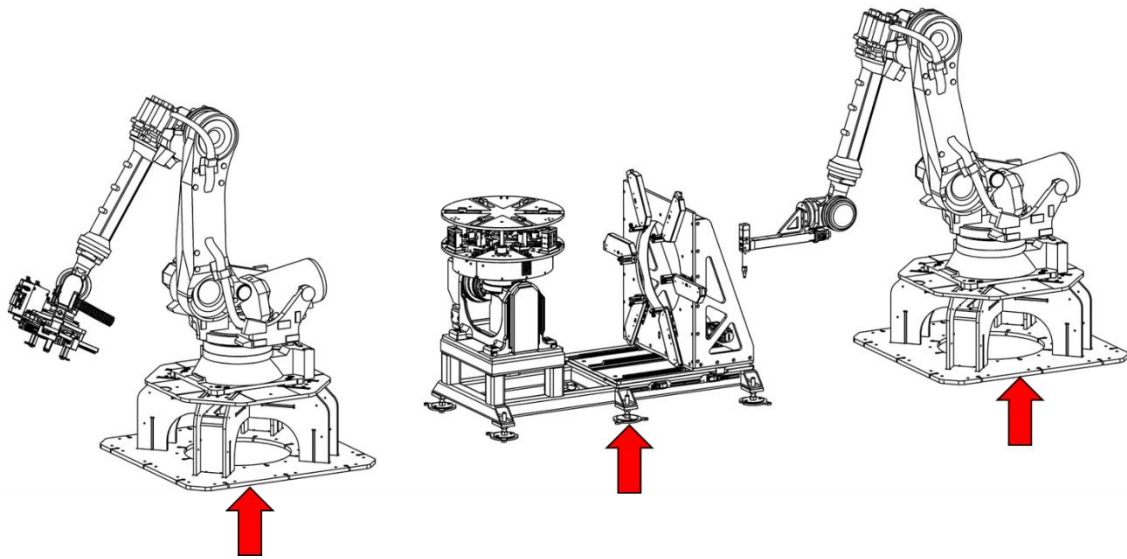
Zonas de fixação ao solo do grupo de aplicação de *sealant* em pneus | Ground fixing zones of Tire sealant application group.
